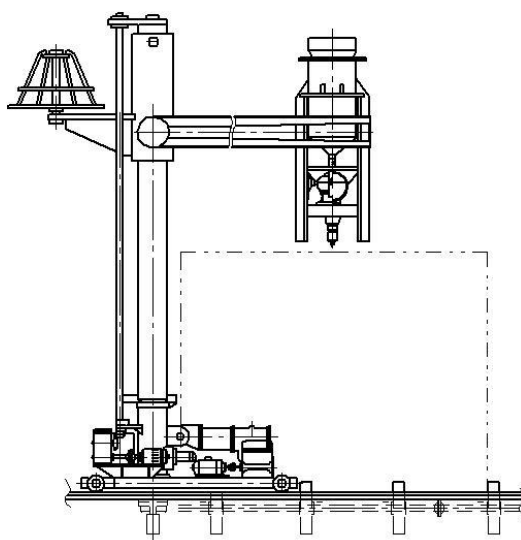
Схема выполнения сварки продольного стыка
